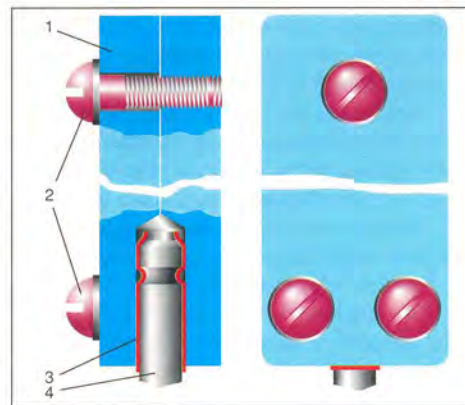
Один из способов защемления стержня клапана во время притирки: 1 – пластины; 2 – винты 6; 3 – резиновая трубка или намотка изоляционной ленты; 4 – стержень клапана.
